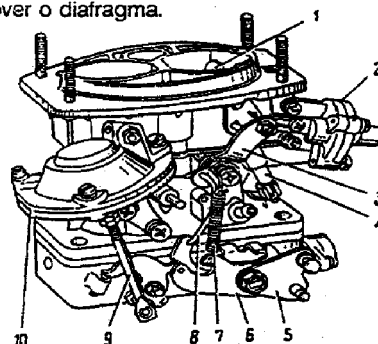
Vista externa do carburador: 1 - borboleta do carburador; 2 - dispositivo de partida; 3 - alavanca de comando do afogador; 4 - haste telescópica; 5 - alavanca de acionamento da borboleta primária; 6 - alavanca limitadora da abertura da borboleta secundária; 7 - mola de retorno; 8 - haste de união da borboleta primária com o dispositivo de partida; 9 - haste do acionamento pneumático; 10 - acionador pneumático.
